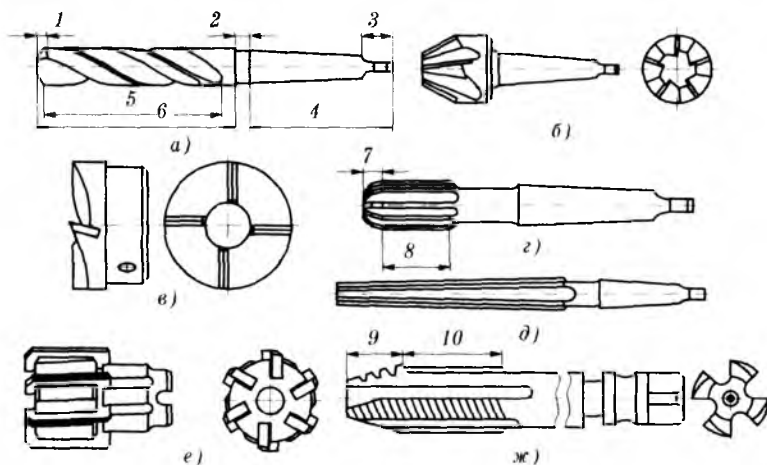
Общий вид инструментов для обработки отверстий:
